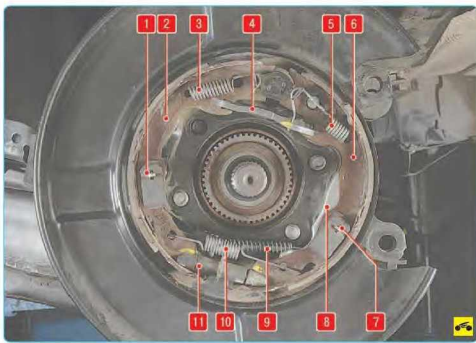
Детали стояночного тормозного механизма: 1, 7 – опорные стойки колодок; 2 – передняя колодка стояночного тормоза; 3 – верхняя стяжная пружина передней колодки; 4 – разжимная планка; 5 – верхняя стяжная пружина задней колодки; 6 – задняя колодка стояночного тормоза; 8 – разжимной рычаг привода тормоза; 9 – задний трос стояночного тормоза; 10 – нижняя стяжная пружина колодок; 11 – регулировочное устройство тормозных колодок стояночного тормоза
